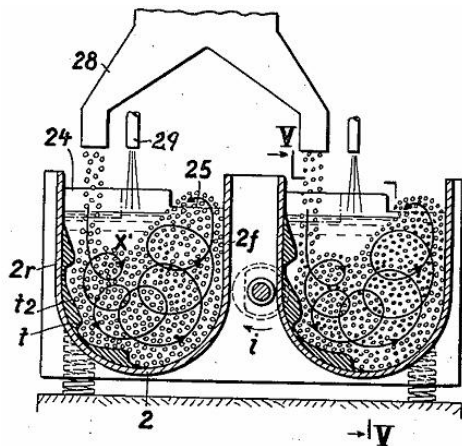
Machine vibratoire avec deux chambres de travail en forme U [28]
